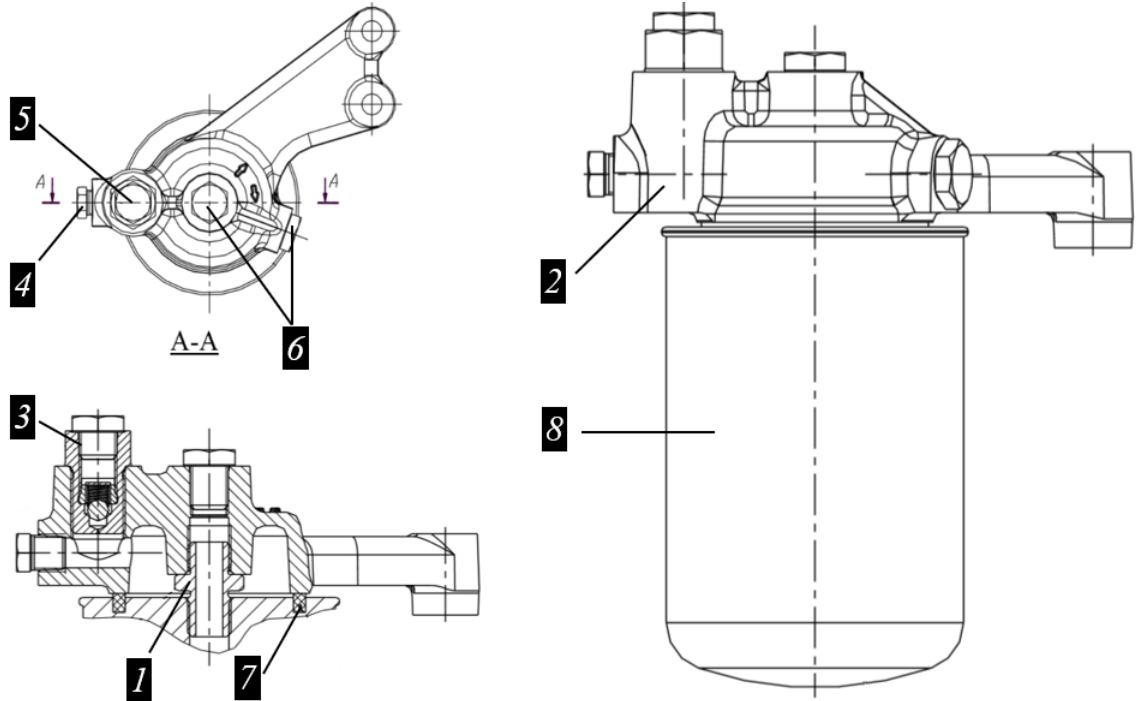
Фильтр тонкой очистки топлива ЯМЗ-236/238
